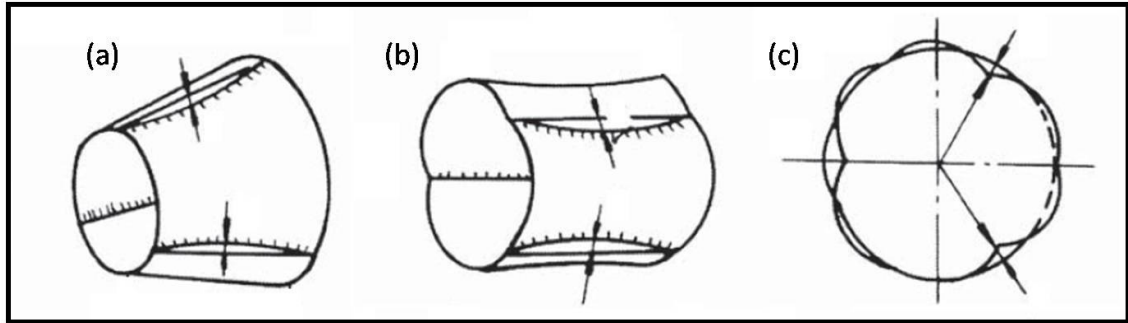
Patrones de distorsión por pandeo en carcasas generados por soldaduras longitudinales. [15]
